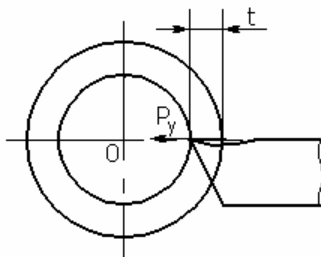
Схема токарной обработки цилиндрической детали:
